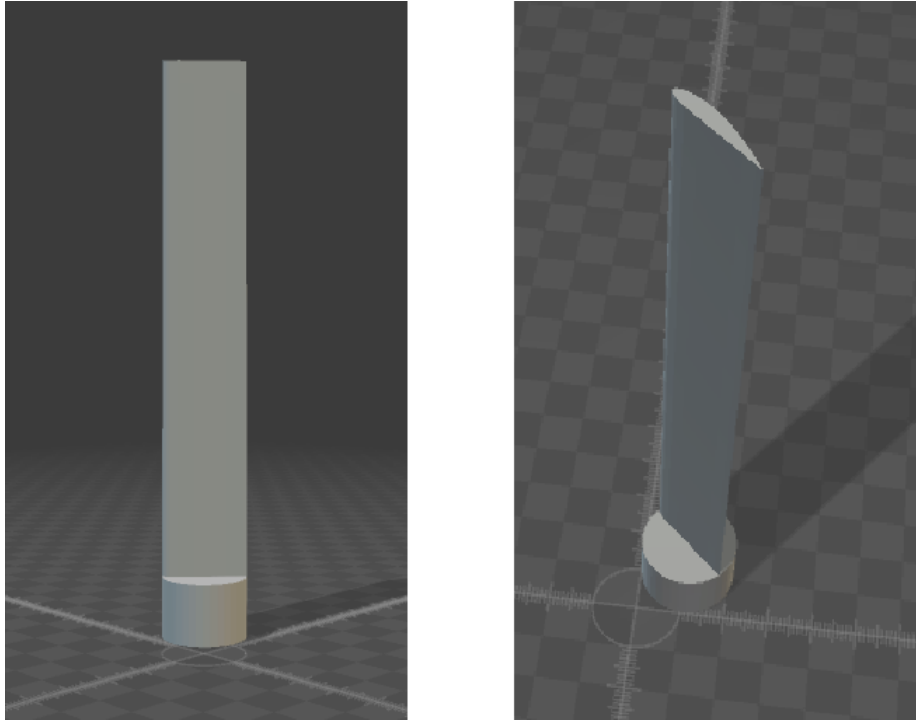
Perfil NACA 4415 após a sua construção digital.
